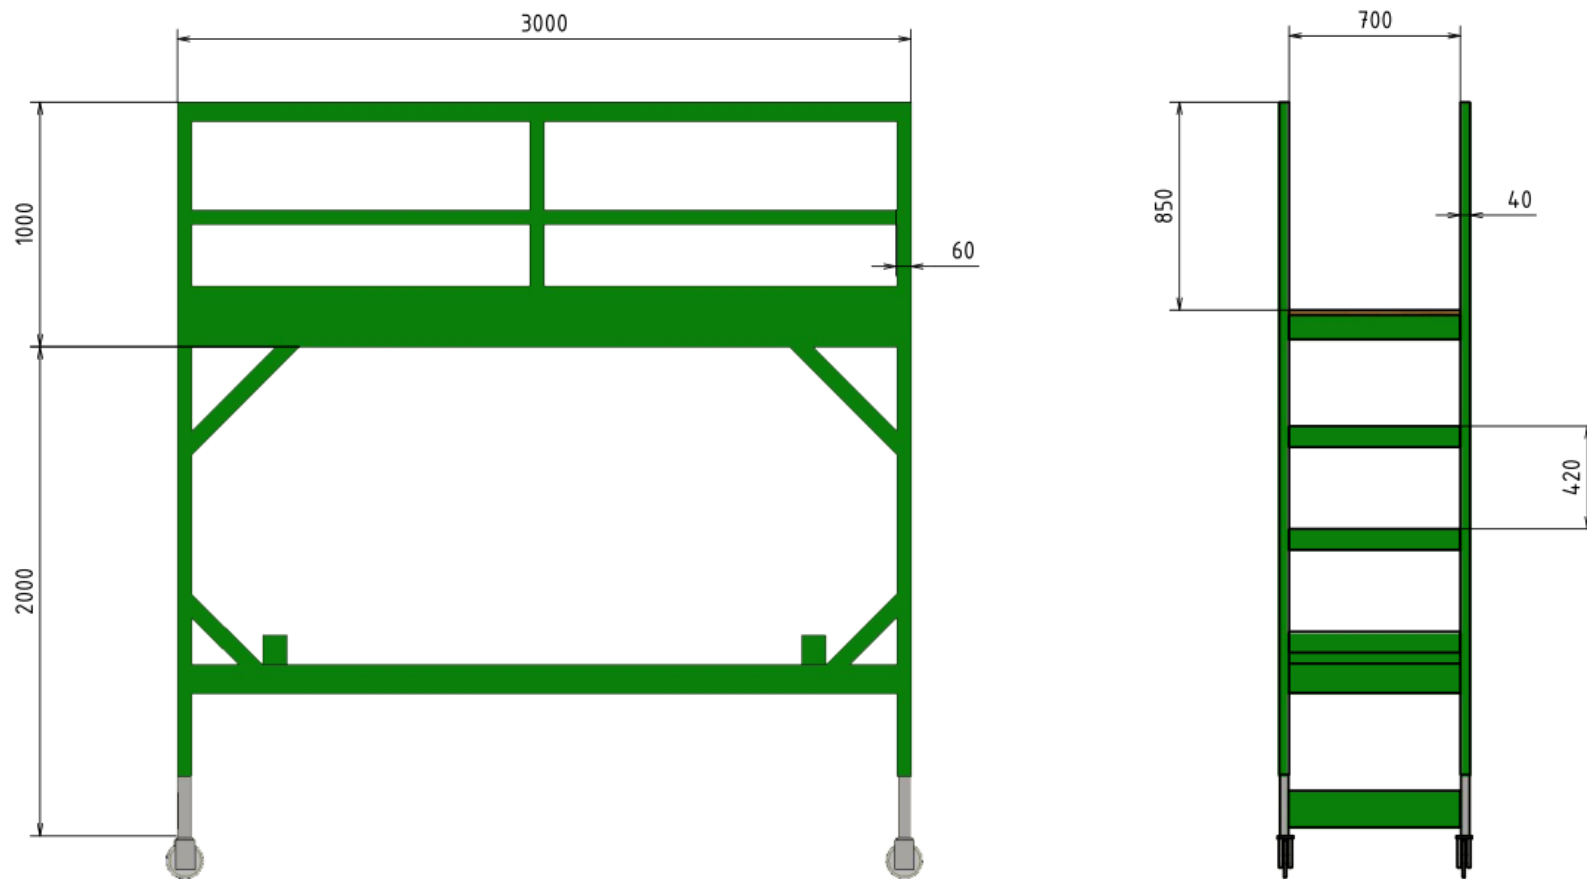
Konstrukce ve výrobní hale [Vlastní tvorba]
